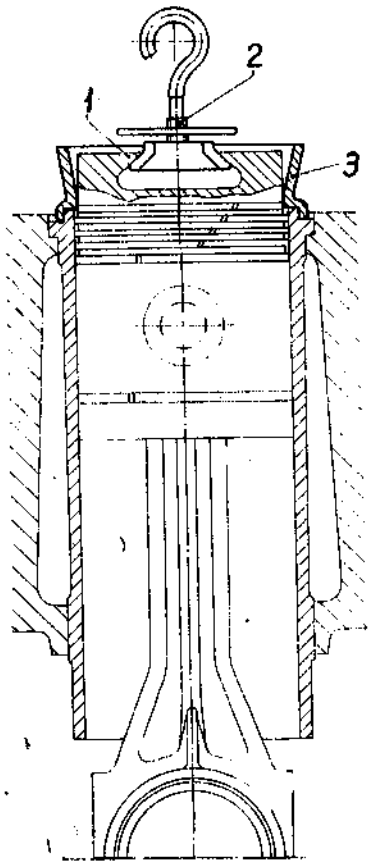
Приспособление для подъема и опускания поршня в цилиндр:
